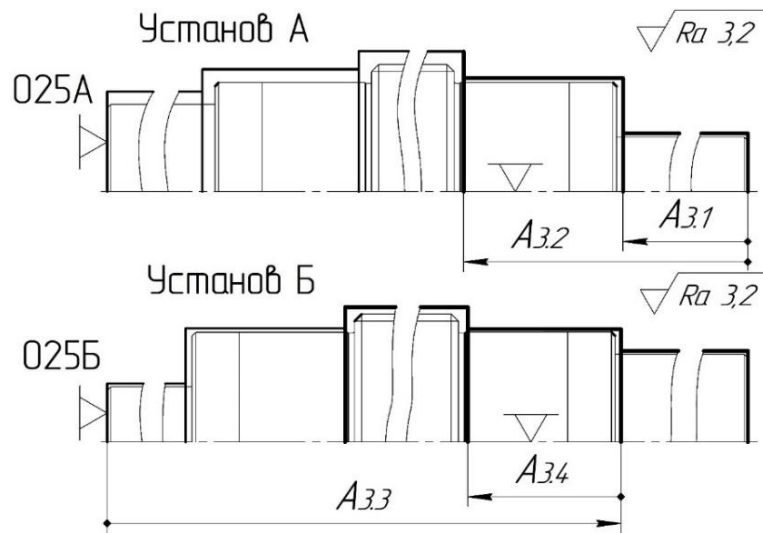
Ескіз заготовки на операції 025 «Токарна з ЧПК»
